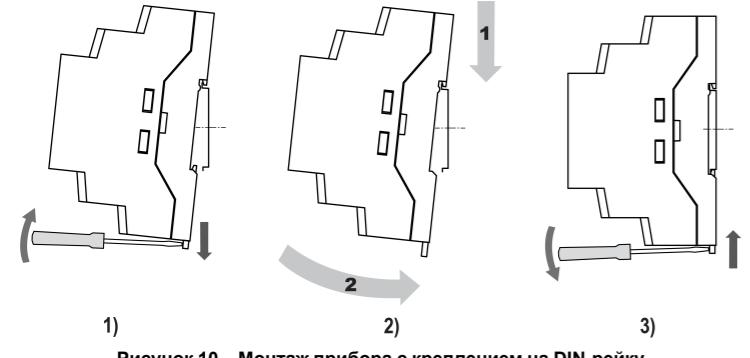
Монтаж прибора с креплением на DIN-рейку
